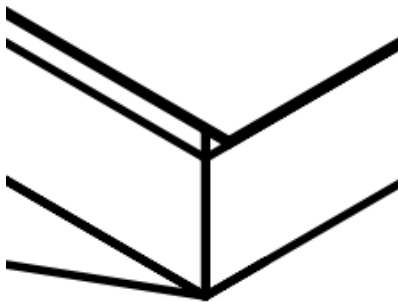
Encaje de vigas de acero A36 UPN 100 cortadas a 45°
